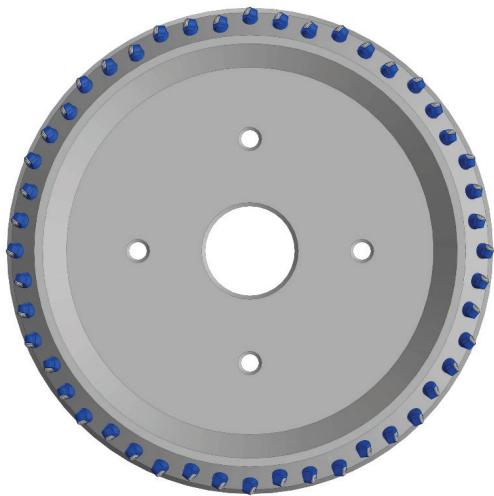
Триступінчаста збірна торцева фреза діаметром 315 мм з похилими циліндричними різальними вставками (3D-модель)
